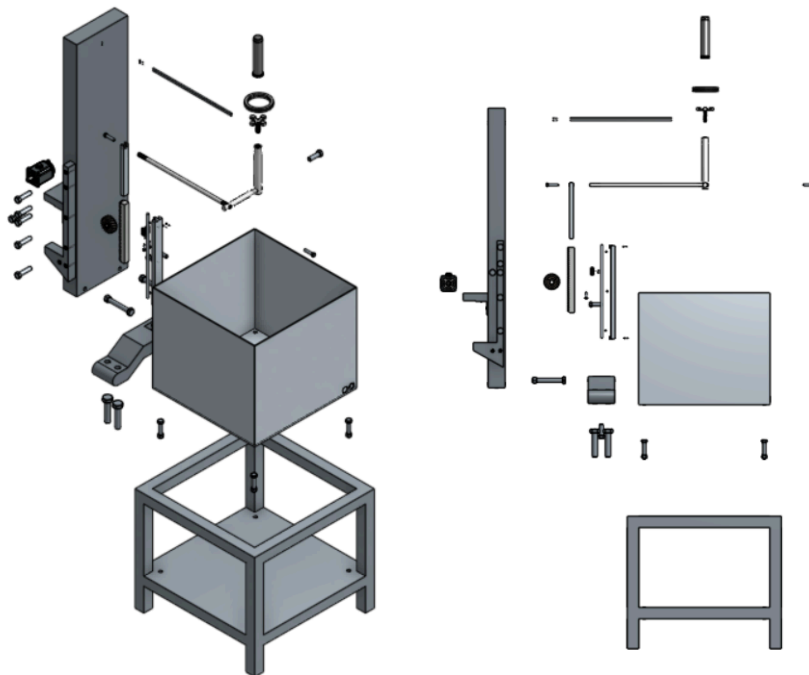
Figura C. A) Vista isométrica explosionada del diseño mecánico final, B) Vista frontal explosionada (Ver planos en el anexo 23)
